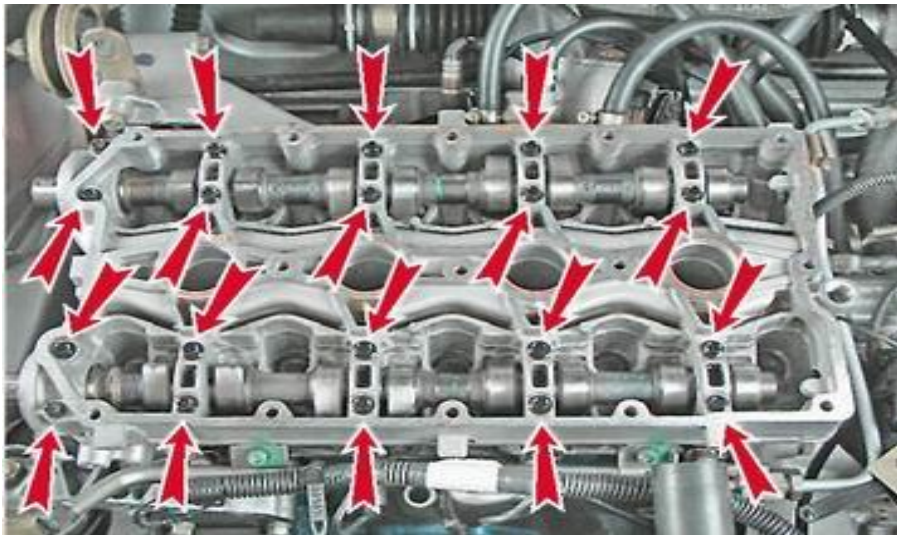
Расположение болтов крепления корпуса подшипников распределительных валов
